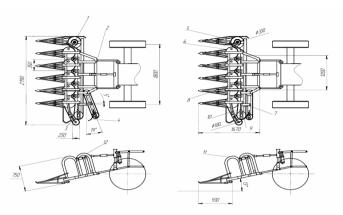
Льнотеребилка ТЛН-1,5А: I— ведущий шкив с коробкой; 2 — ограждение; 3 — цепная передача; 4 — навеска; 5 — карданная передача; 6 — нажимной ролик; 7 — выводящее устройство; 8 — натяжной шкив; 9 — теребильный ремень; 10 — теребильный шкив; 11 — делитель; 12 — рама [5]
